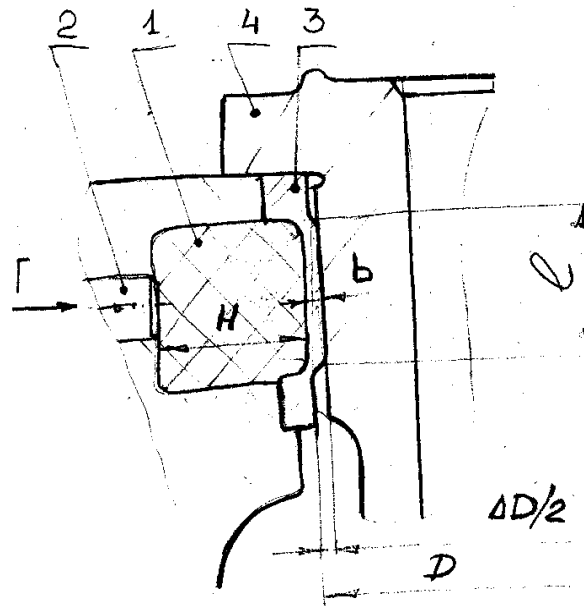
Гідропластичний затискач: 1 – гідро-пласт; 2 - плунжер; 3 – втулка металева; 4 – гільза.
